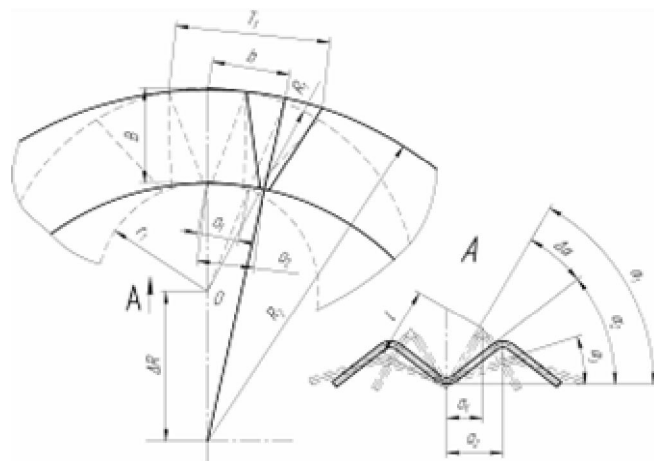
Розрахункова схема відпружинення профільної гвинтової заготовки
